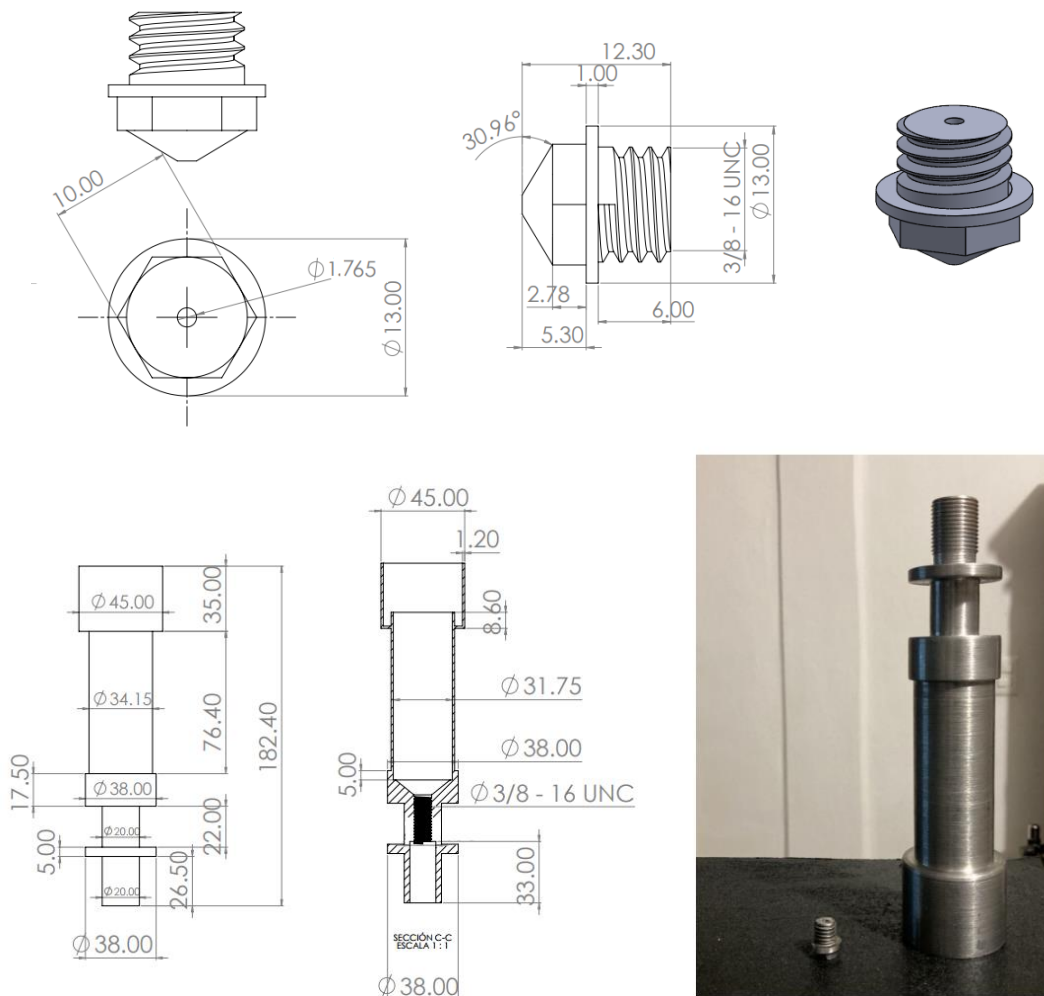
Diseño CAD del recipiente y boquilla para el viscosímetro Saybolt Universal.
